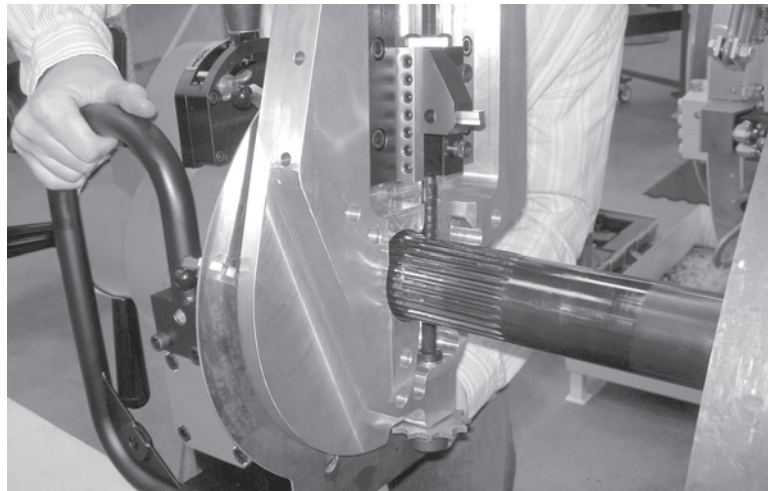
Posizionare la macchina EP 424 per il montaggio sull'albero.
